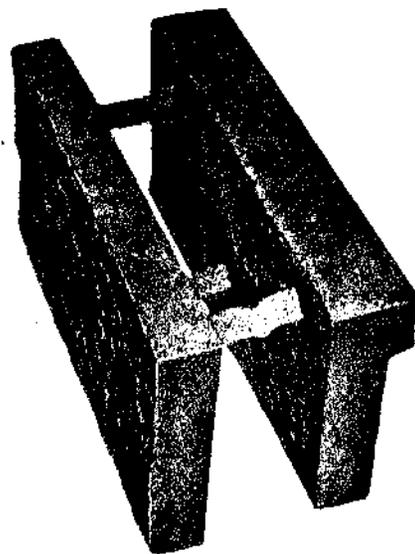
Pieza soldada en un horno rotatorio.
